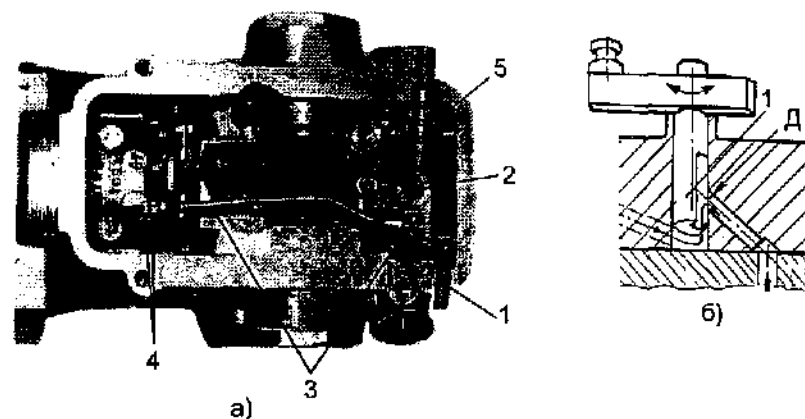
Форма дозатора и его расположение в корпусе насоса модели DPC Serie 048391BA фирмы "Roto-Diesel":
